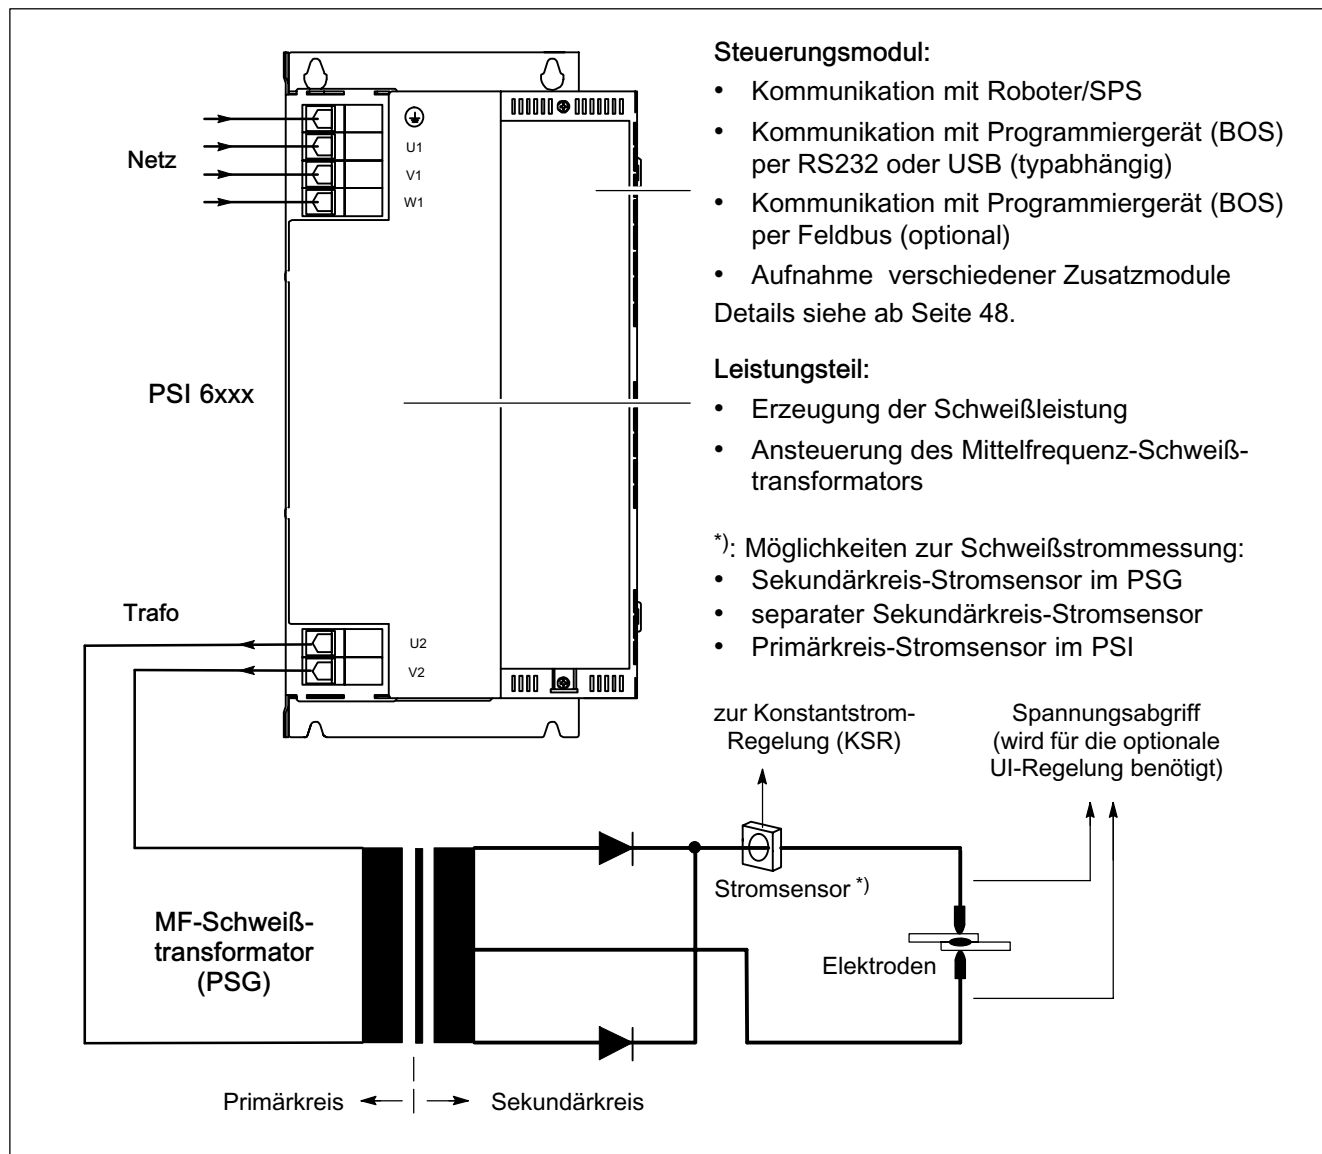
Prinzipieller Aufbau einer MF-Schweißeinrichtung mit PSI 6xxx
